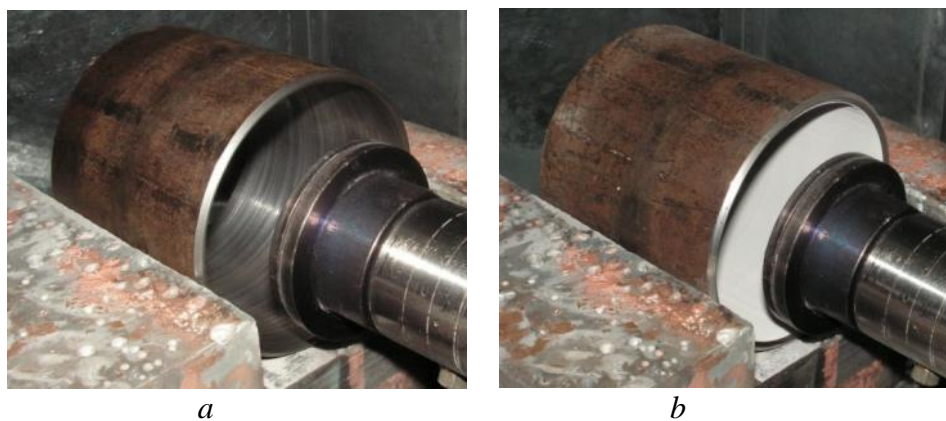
Образец трубы с алюминиевым покрытием
